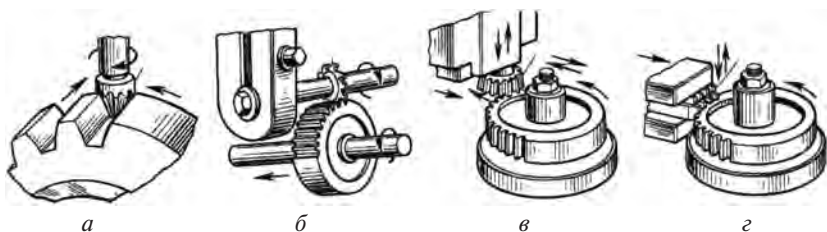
Изготовление зубчатых колес копированием с помощью фрез (*а, б*) и обкаткой с помощью долбяка и гребенки (*в, г*):
